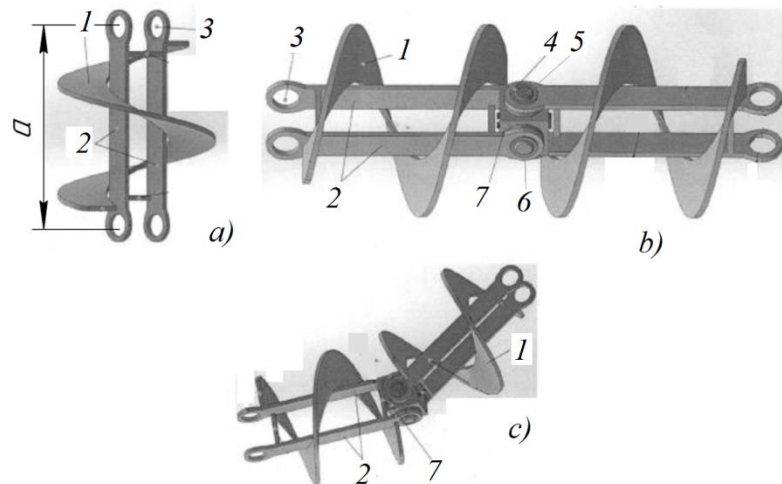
Схематизації комплектування гнучкого шнекового механізму із окремих секцій: 1 – робоча поверхня шнека; 2 – пластини; 3 – отвори; 4 – втулки; 5, 6 – пальці; 7 – квадратна основа;
